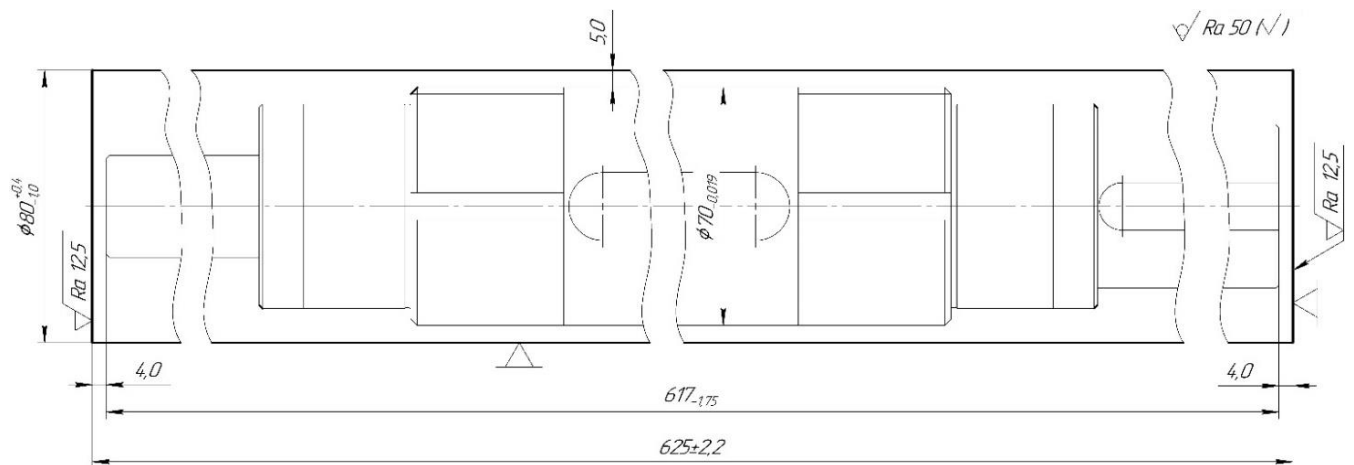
Заготовка, яка виготовлена із круглого прокату
